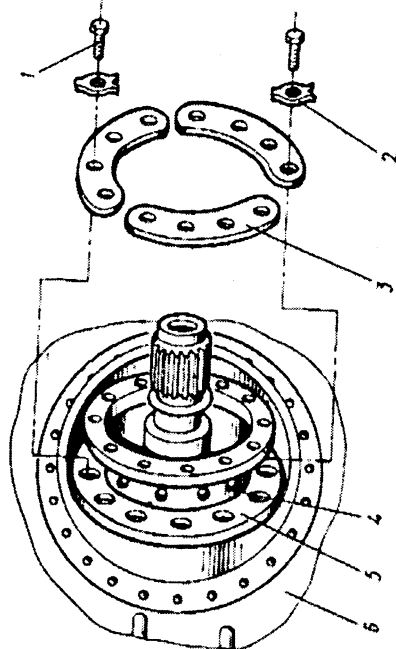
Узел соединения выходного патрубка с фланцем корпуса трансмиссии:
